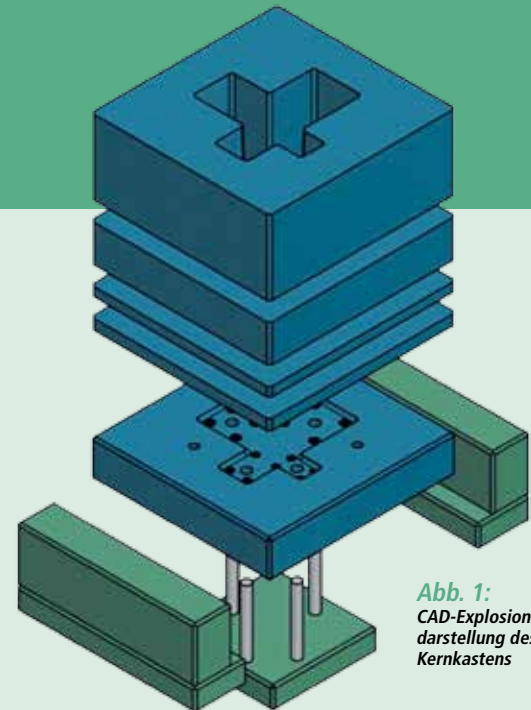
CAD-Explosionsdarstellung des Kernkastens
